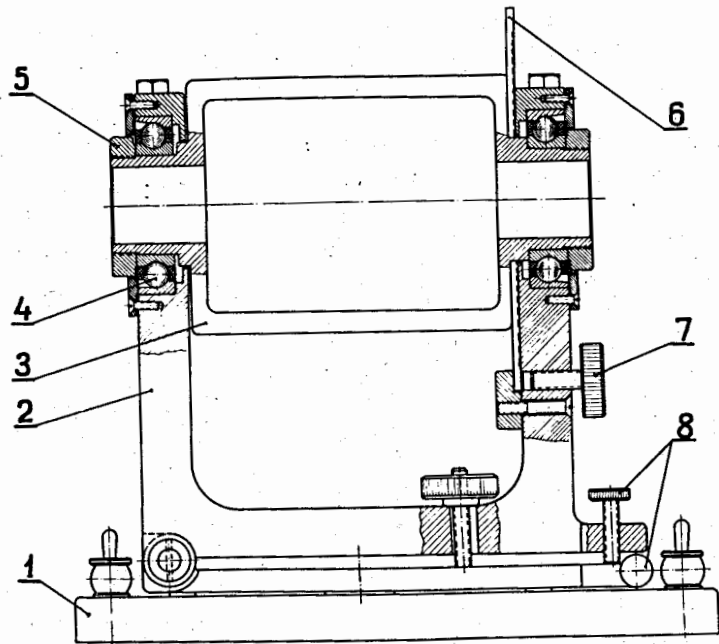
Юстировочная установка: 1 - основание; 2 - корпус; 3 - рама; 4 - шарикоподшипник; 5 - гайка; 6 - угловая шкала; 7 - фиксирующий винт; 8 - винты для выверки оси вращения.
